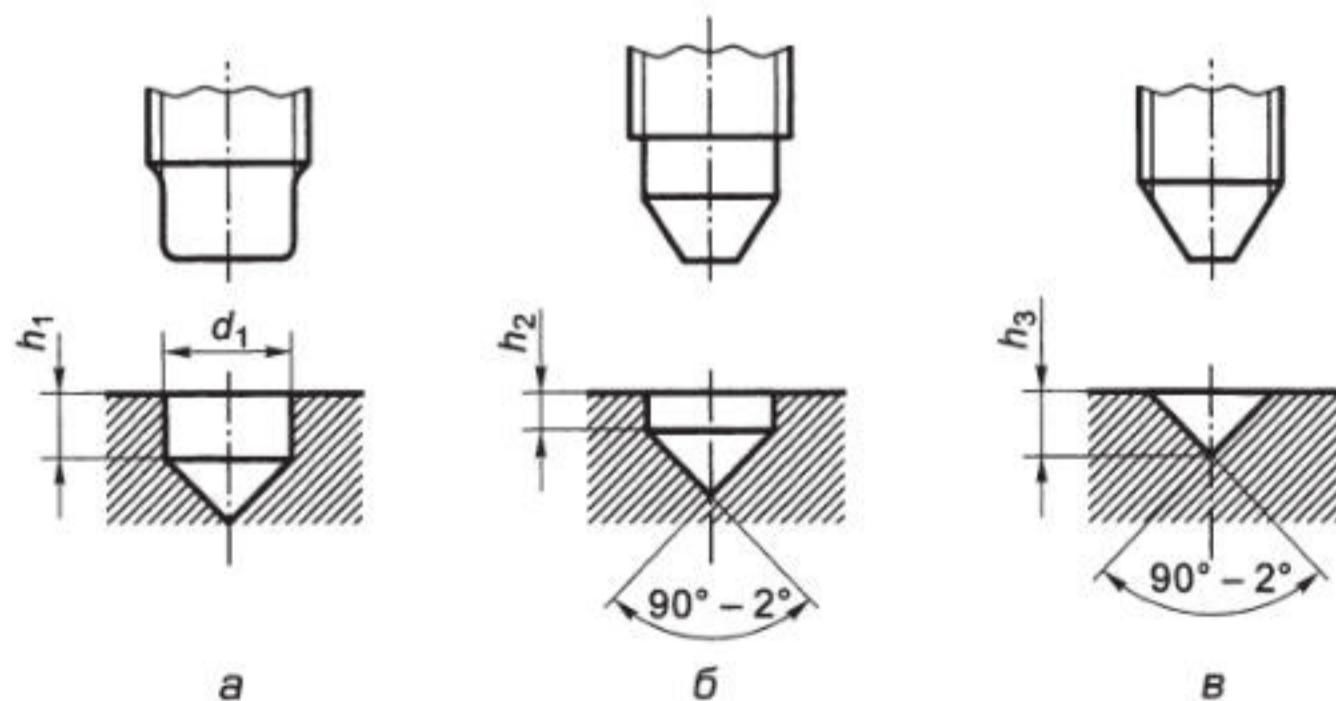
Отверстия под концы винтов, болтов и шпилек с цилиндрическим [а], цилиндрическим с фаской [б] и коническим [в] концами
